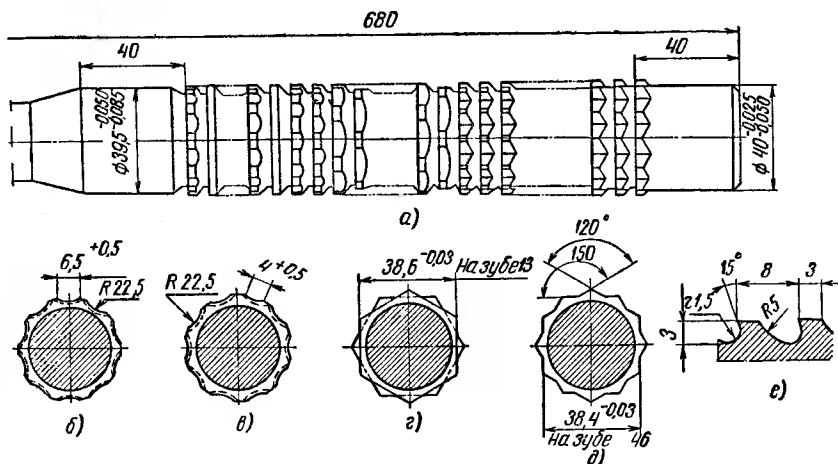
Протяжка для протягивания 12-гранного отверстия:
